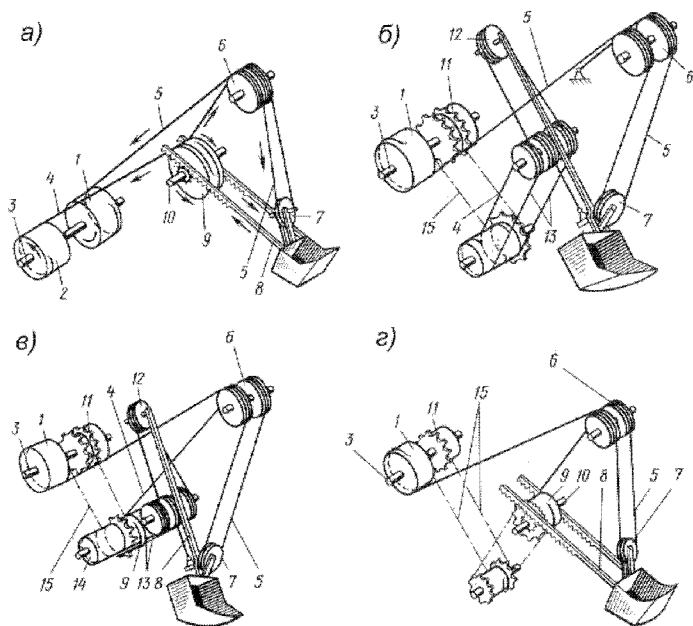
Схемы напорных механизмов экскаваторов с гибкой подвеской прямой лопаты:
